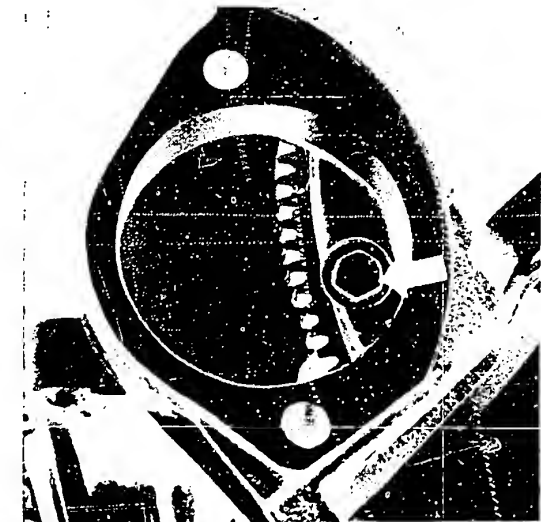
Bei Fahrzeugen mit Automatikgetrieben müssen die Schrauben des Drehmomentwandlers nach dem Entfernen des Anlassers (Starter) durch die Öffnung im Motorgehäuse gelöst werden.
